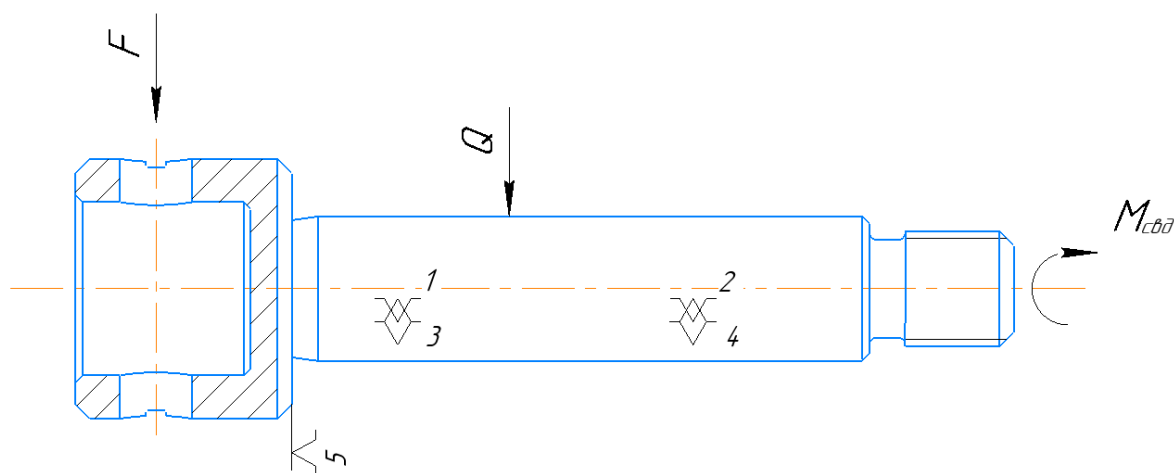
Принципиальная схема зажима заготовки в приспособлении с указанием мест приложения силы зажима  $Q$ .
